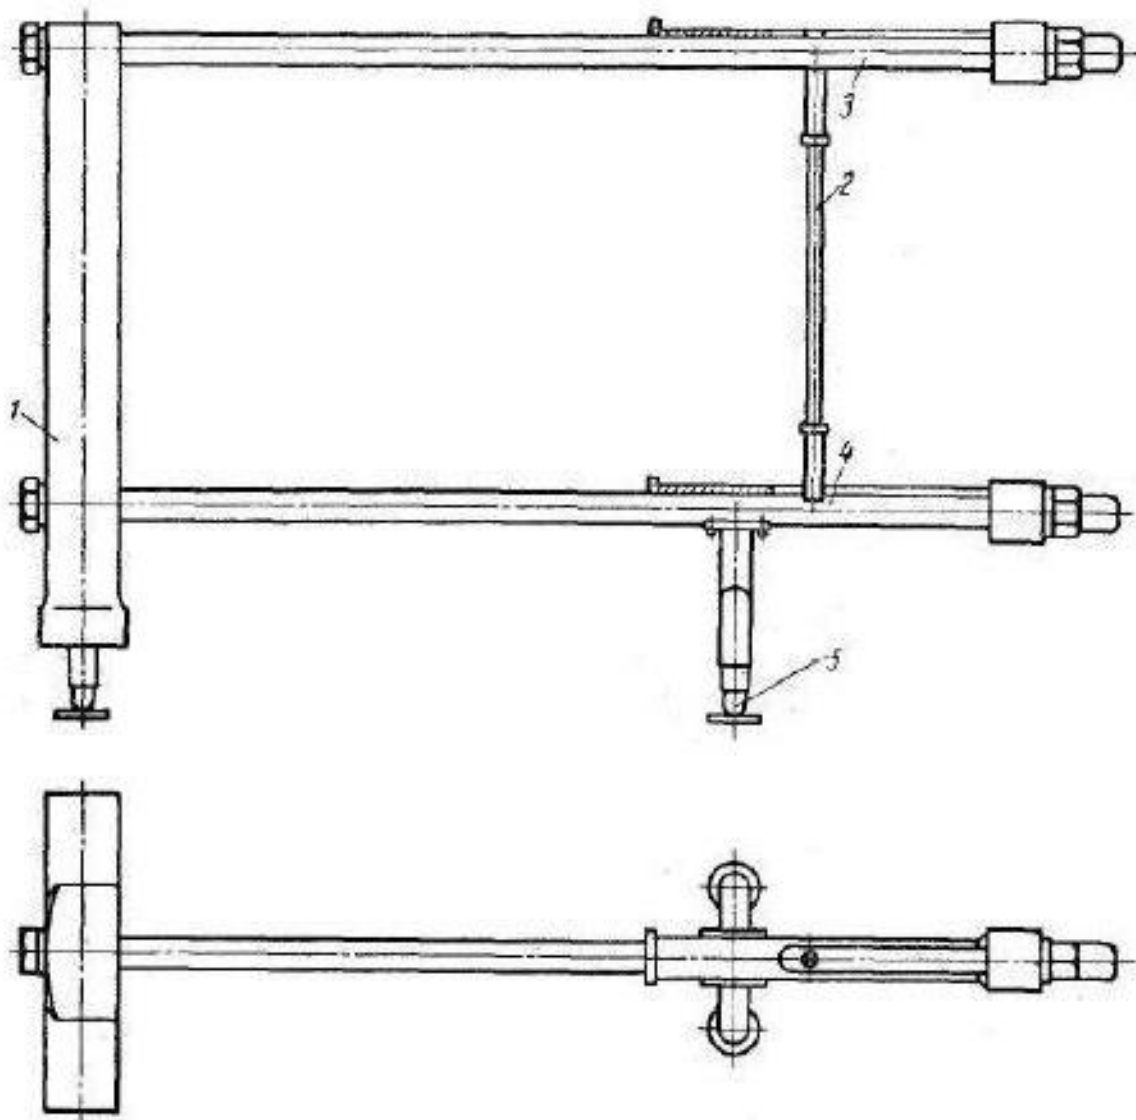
Рама пластинчатого теплообменника: 1 – опорная плита (стойка); 2 – распорка; 3,4 – верхняя и нижняя штанга с накладками; 5 – опора; 6 – зажимной механизм
